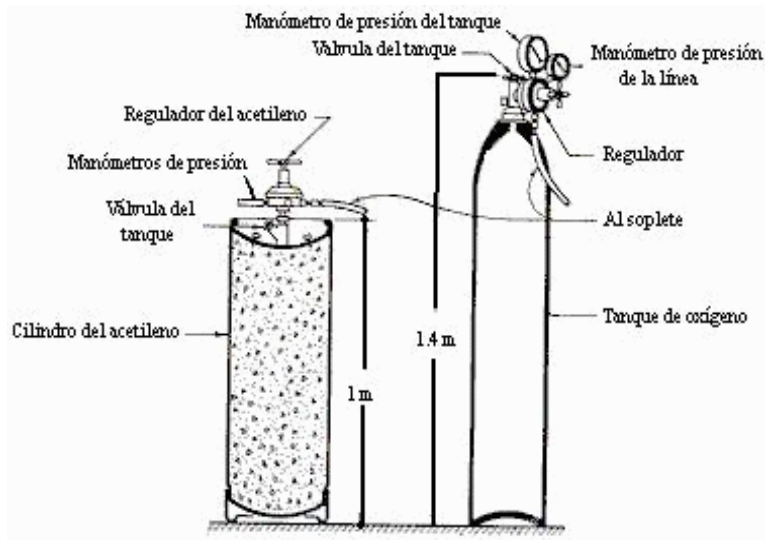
Cilindros y reguladores para soldadura oxiacetilénica
